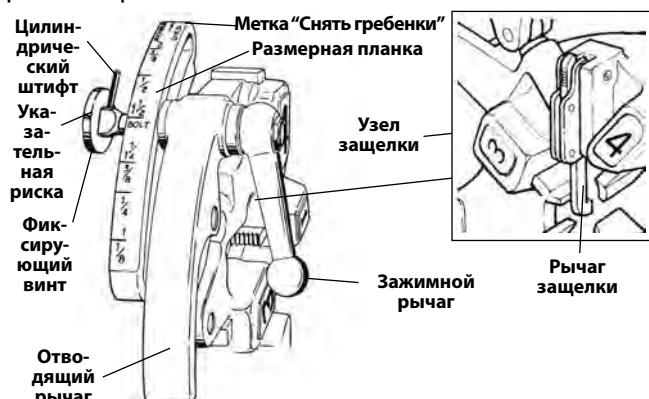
Универсальная самооткрывающаяся резьбонарезная головка
